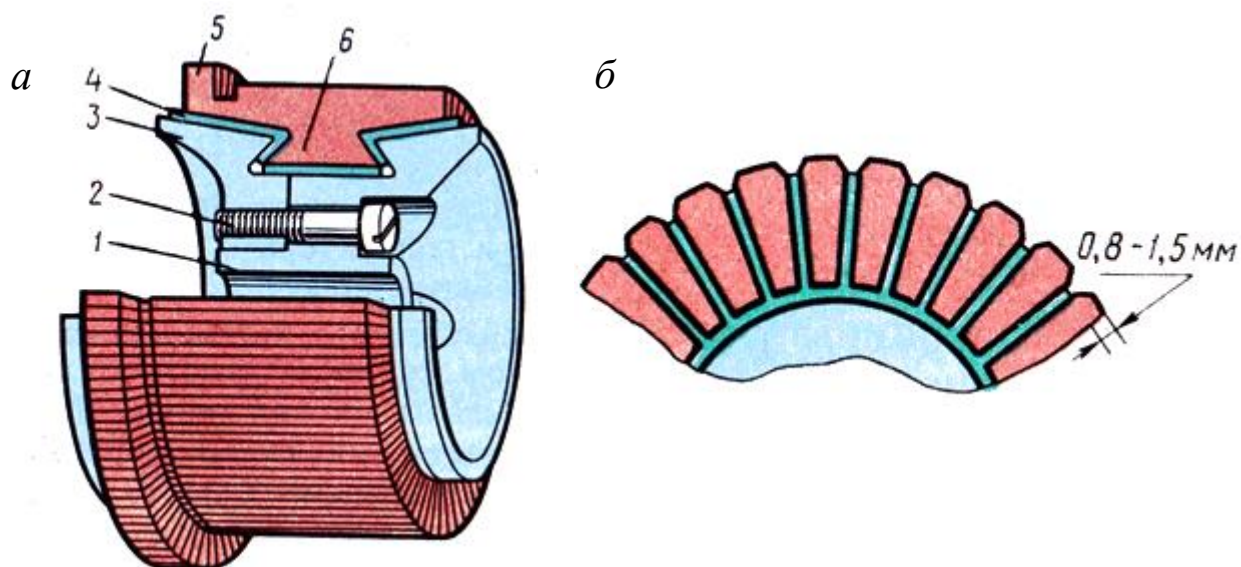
Конструкція колектора з конусним шайбами
